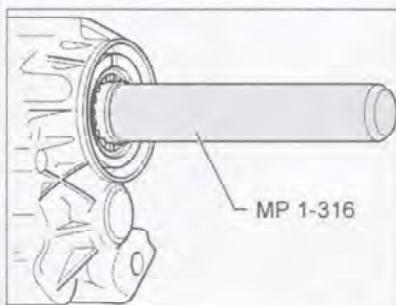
Нагрев 2-ю внутреннюю обойму подшипника первичного вала до 100°C, напрессуйте ее на вал.
